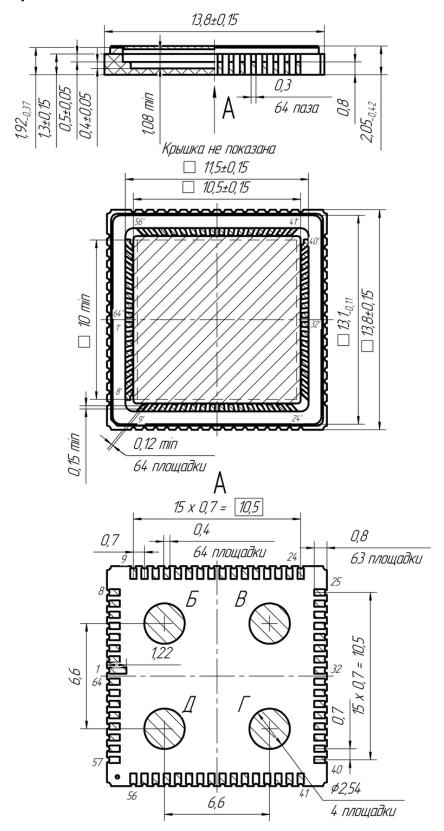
Габаритный чертеж корпуса 5153.64-3 (размеры в мм)
